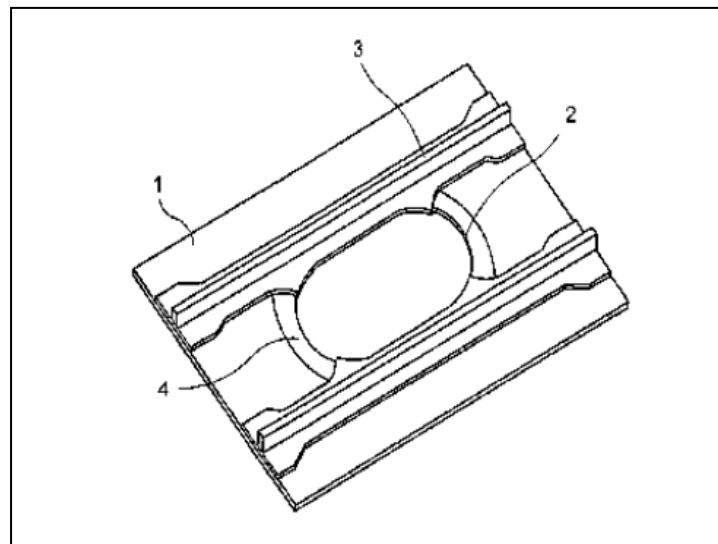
Detalles de los refuerzos que completan el borde de fijación para una puerta de acceso. Fuente: US2009166473.
